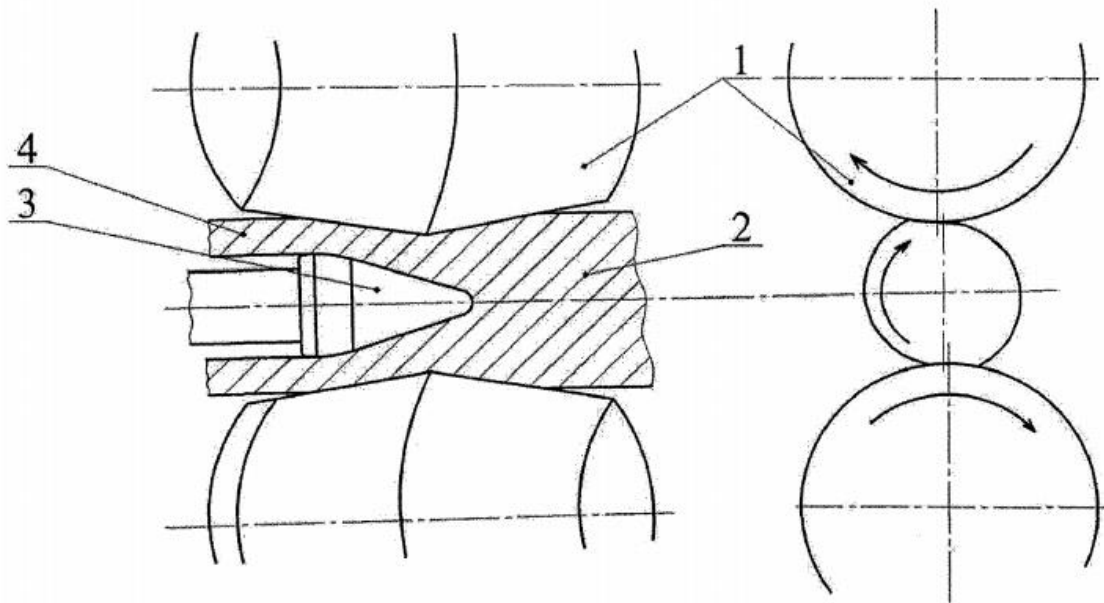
Схема процесса прошивки в стане с бочковидными валками: 1 – валки; 2 – заготовка; 3 – оправка; 4 – гильза
